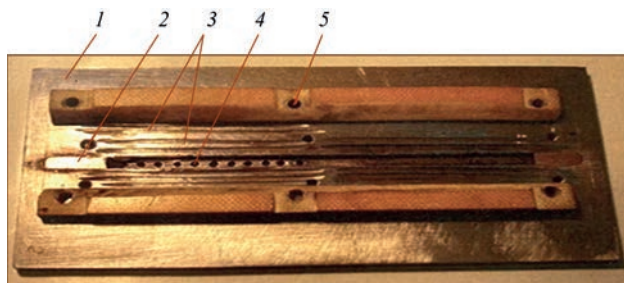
Спеціальне пристосування для фіксації: 1 – пластина з нержавіючої сталі; 2 – мідна вставка для збудження дуги на початку зварювання; 3 – поздовжні пази для зниження тепловідводу від зразка який зварюється; 4 – поздовжній паз з отворами для піддуву аргону до кореня шва; 5 – текстолітові притискні губки для закріплення зразка
